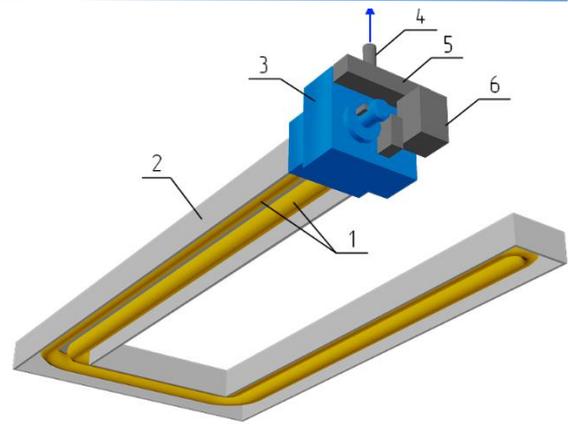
Ленточный инфракрасный двухтрубный газовый нагреватель марки EUCERK:
